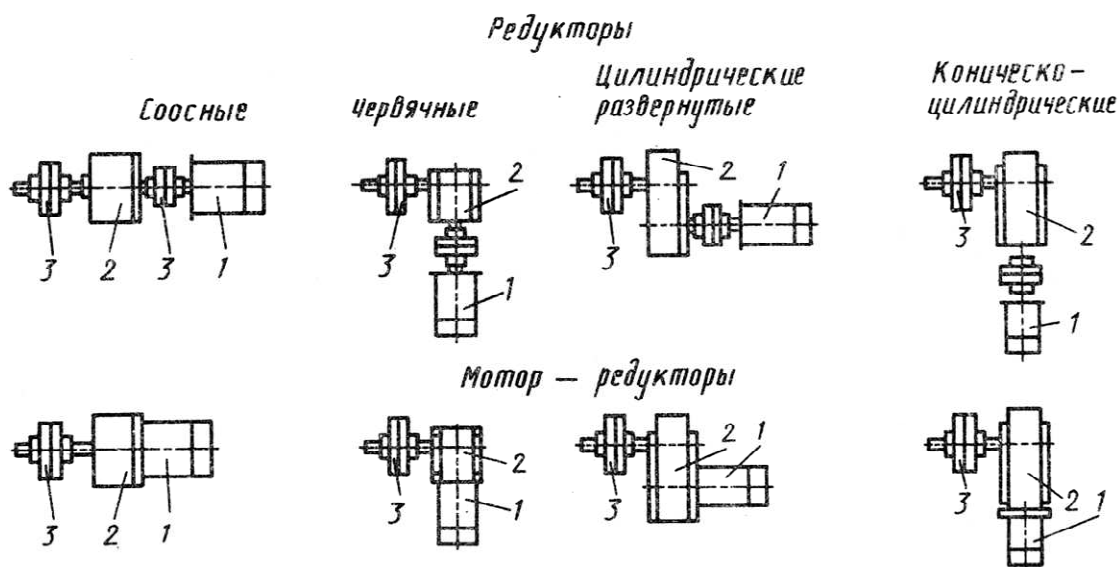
Компоновочные схемы приводов с применением редукторов и мотор-редукторов: 1 – электродвигатель; 2 – редуктор; 3 – муфта
